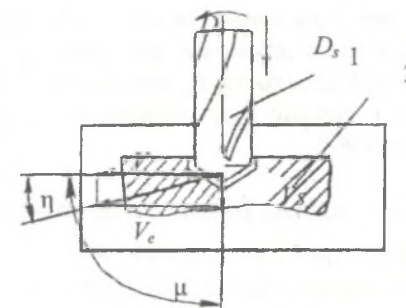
Кинематика сверления: 1 – режущий инструмент (сверло); 2 – обрабатываемое изделие.
